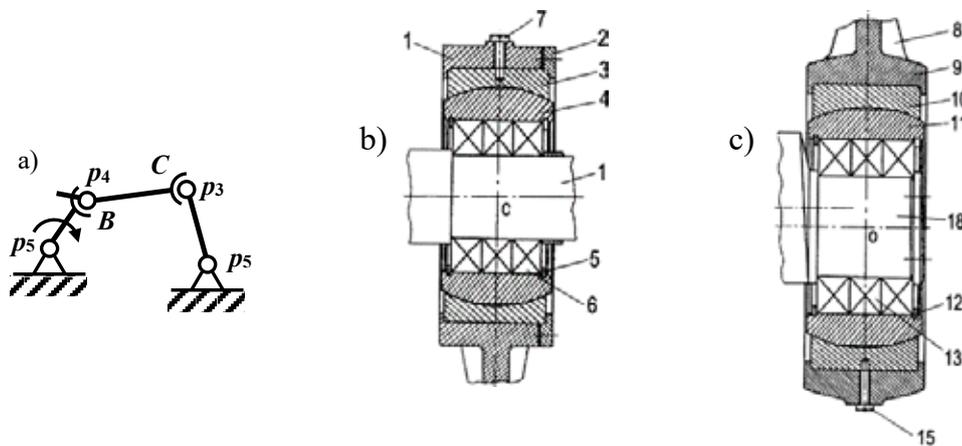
Структурная схема самоустанавливающегося четырехзвенного механизма с условным изображением кинематических пар (а), конструкция кинематической пары p_3 (b), конструкция кинематической пары p_4 (с)
